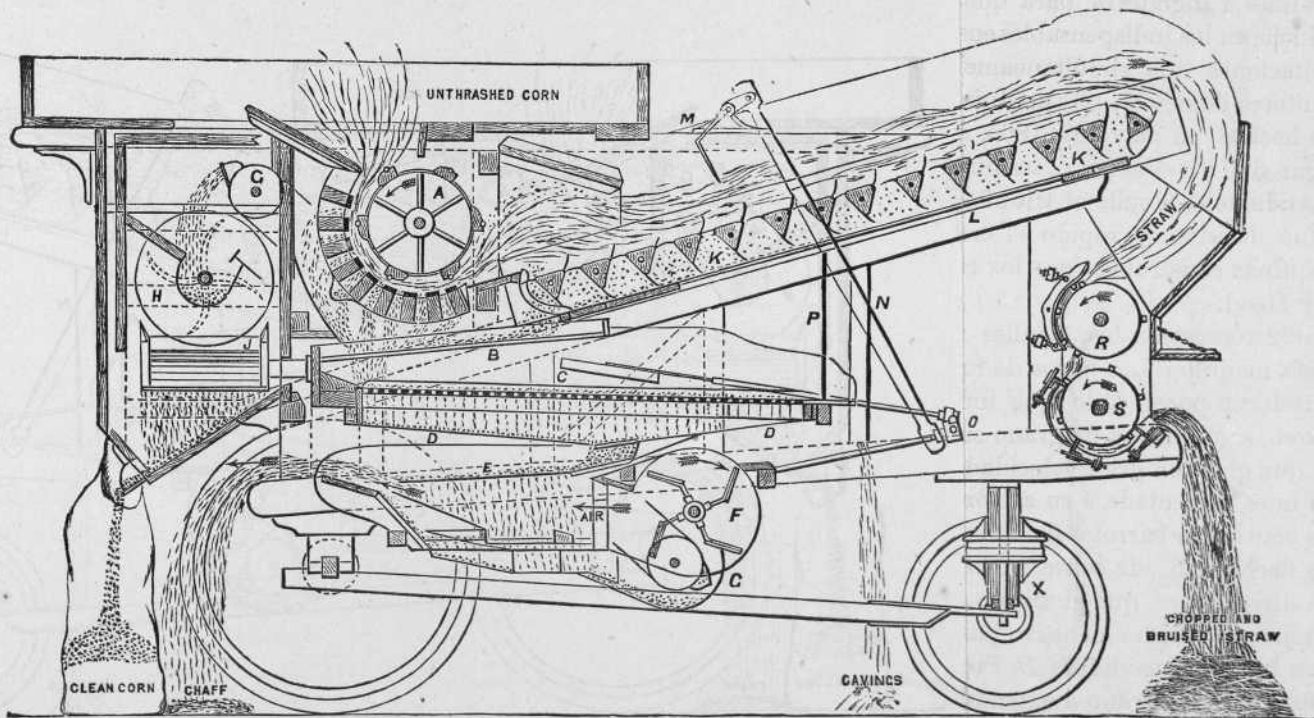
Detalles mecánicos de la trilladora marca H. de Ransomes.
